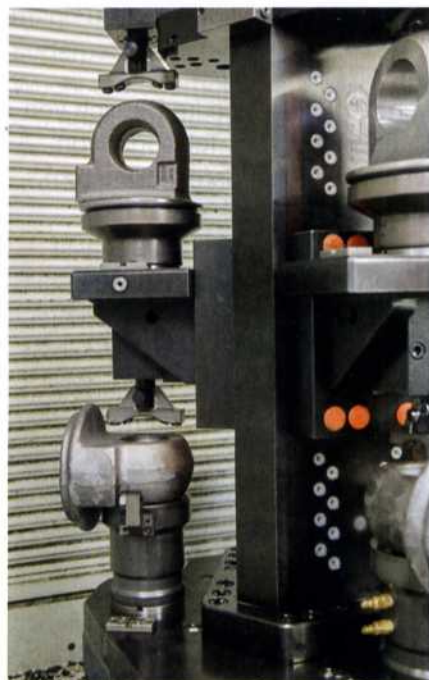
Von oben werden die unterschiedlichen Werkstücke mit einem Druckstück hydraulisch fixiert
